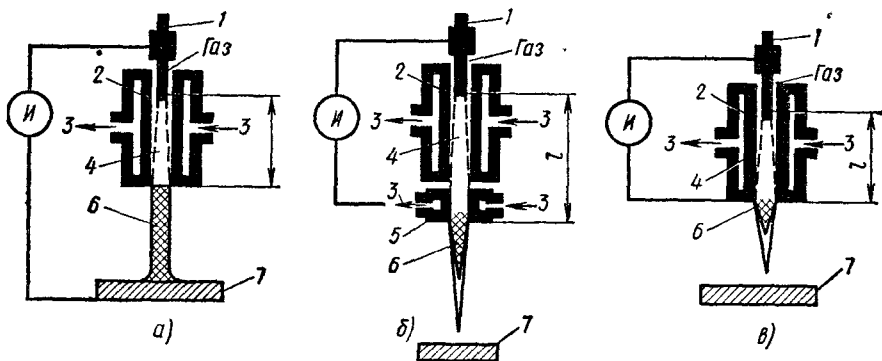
Схемы сварки плазменной дугой (а) и плазменной струей (б, в):
